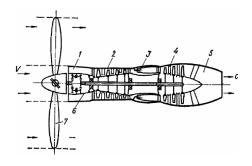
Схема самолетного ТВД: I — входное устройство; 2 — компрессор; 3 — камера сгорания; 4 — газовая турбина; 5 — выходное устройство; 6 — редуктор; 7 — воздушный винт
